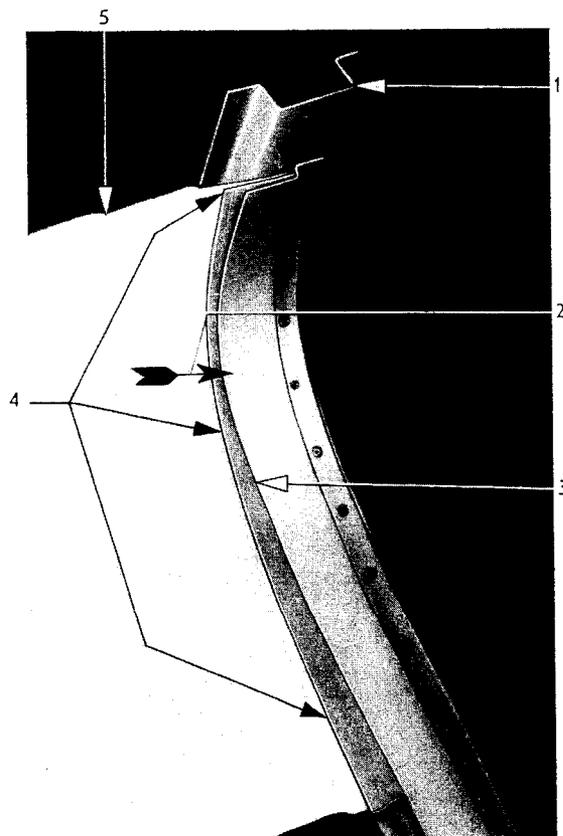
Himmel mit aufgenähtem Pappstreifen in hinteren Dachspriegel einschieben - Caravan
